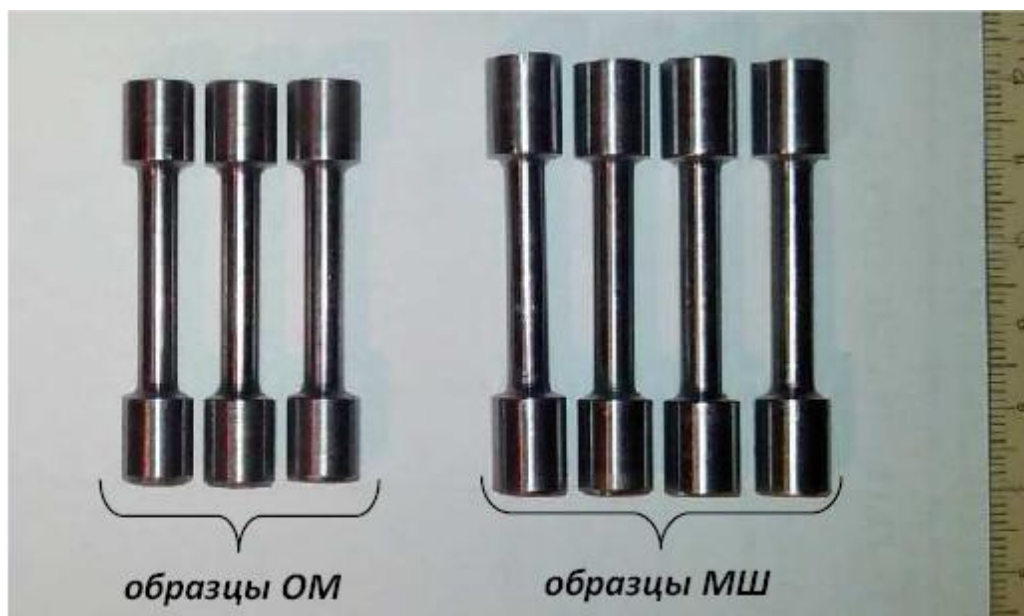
Цилиндрические образцы основного металла и металла сварного шва
